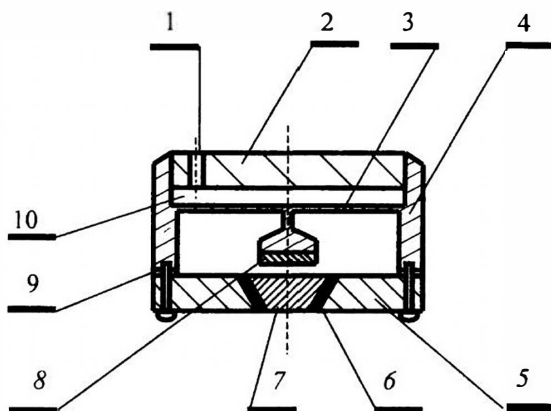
Двухступенчатый ёмкостный датчик давления: 1 — капилляр в пробке 2, 3 — мембрана корпуса 4, 5 — основание, 6 — изолирующая плёнка, 7 — конус (обкладка конденсатора); 8 — пластина (обкладка конденсатора), 9 — прокладка; 10 — подмембранная камера
